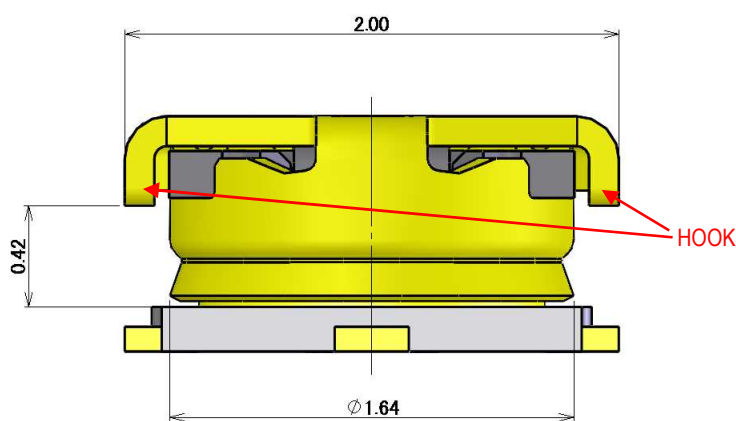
挿抜 JIG 引っ掛け形状配置図 / PLUG connector with hooks for pulling jig
